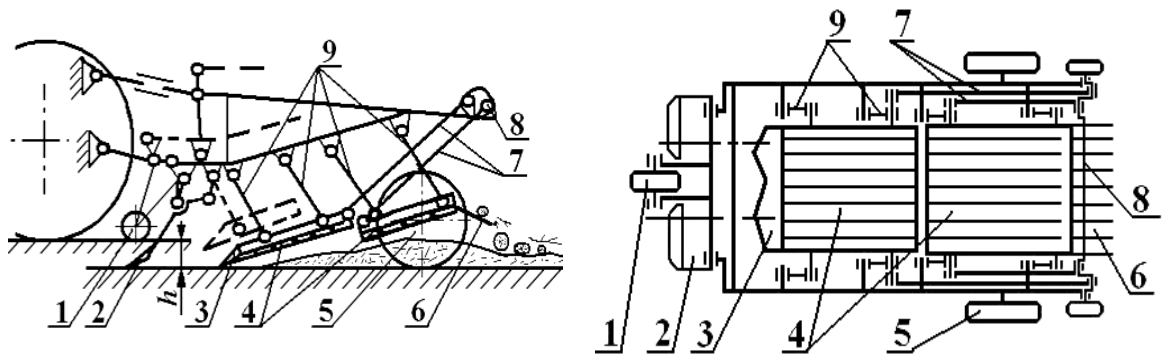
Схема грохотного копача: 1 – опорний коток; 2 – запобіжна напівскоба; 3 – леміш; 4 – дворешітний грохот; 5 – опорне колесо; 6 – струшувальна решітка; 7 – шатуни; 8 – ексцентриковий вал; 9 – підвіски решета
